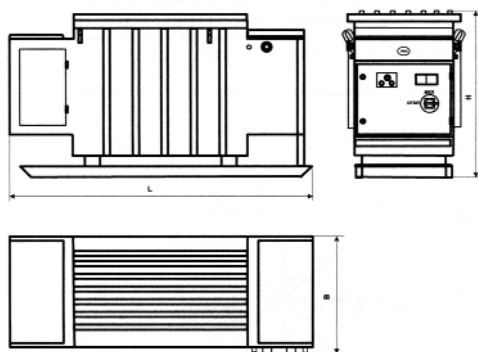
Габаритные размеры подстанции типа КТП-РН
